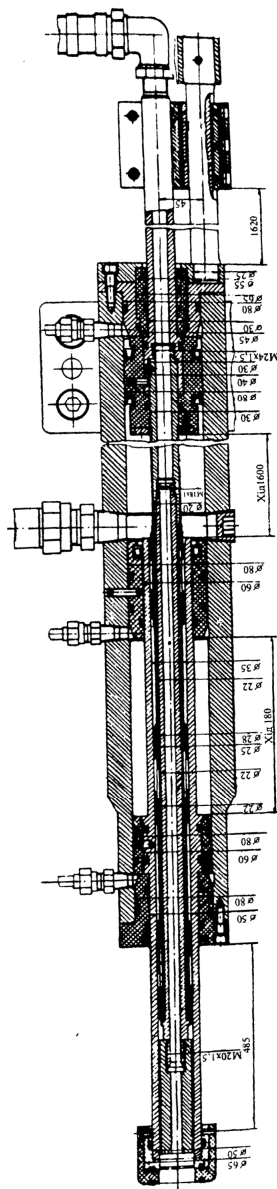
Інструментальна головка верстату «Дуга-13» (розріз)
